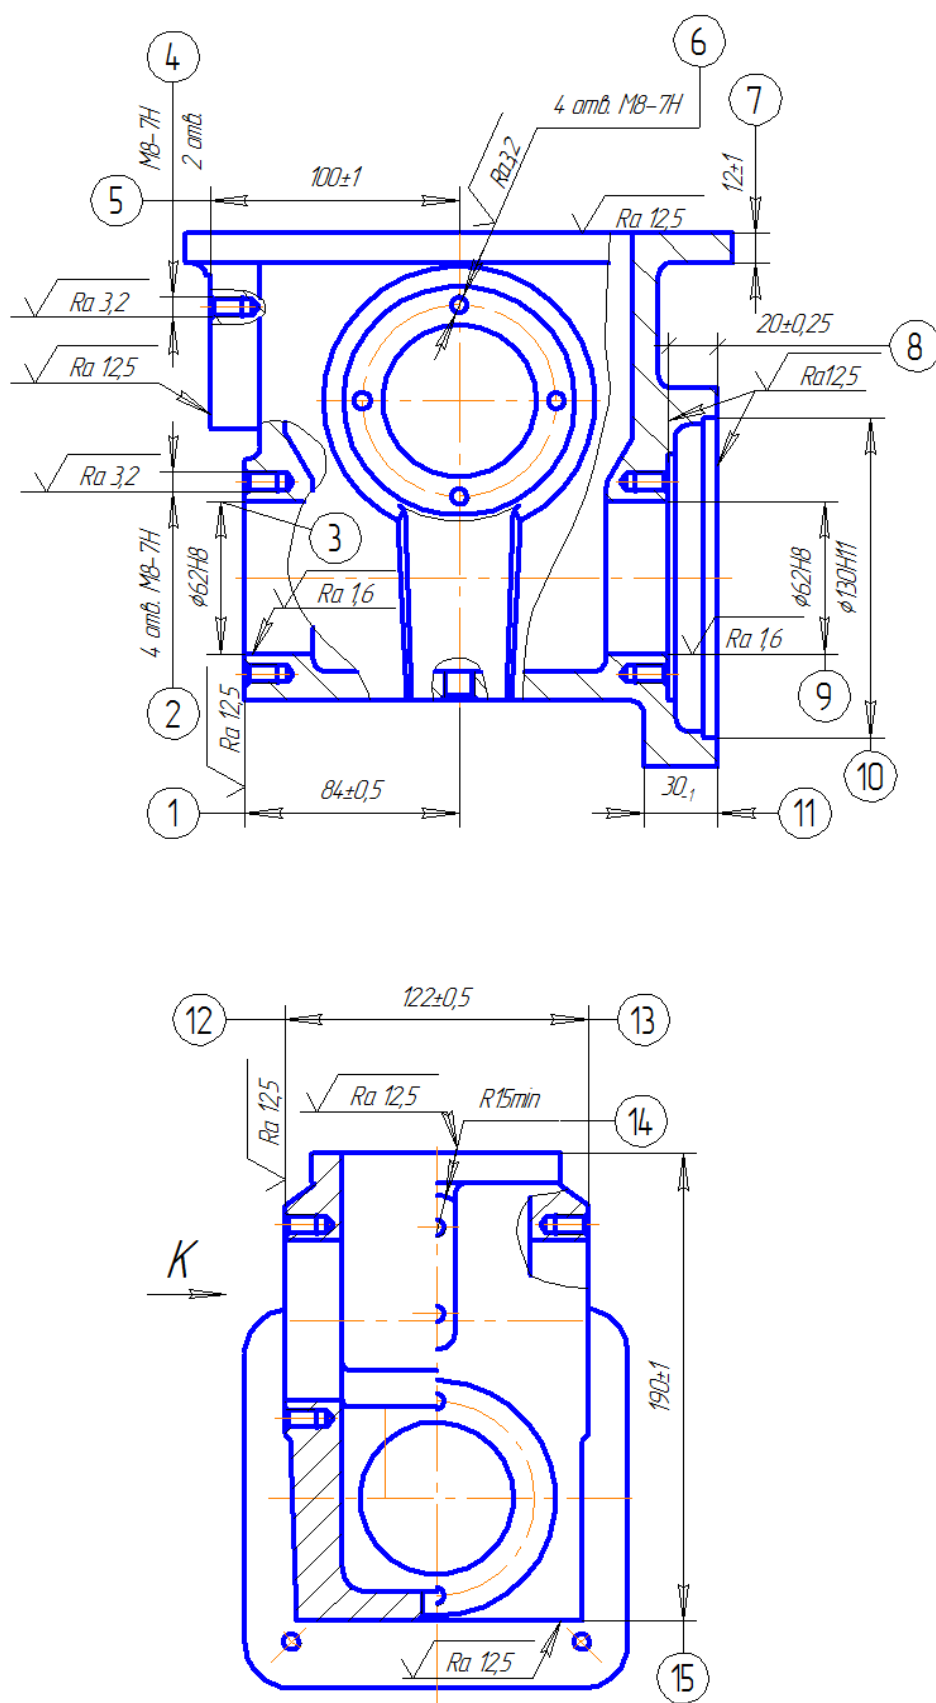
Эскиз детали «Корпус редуктора водяной помпы»
